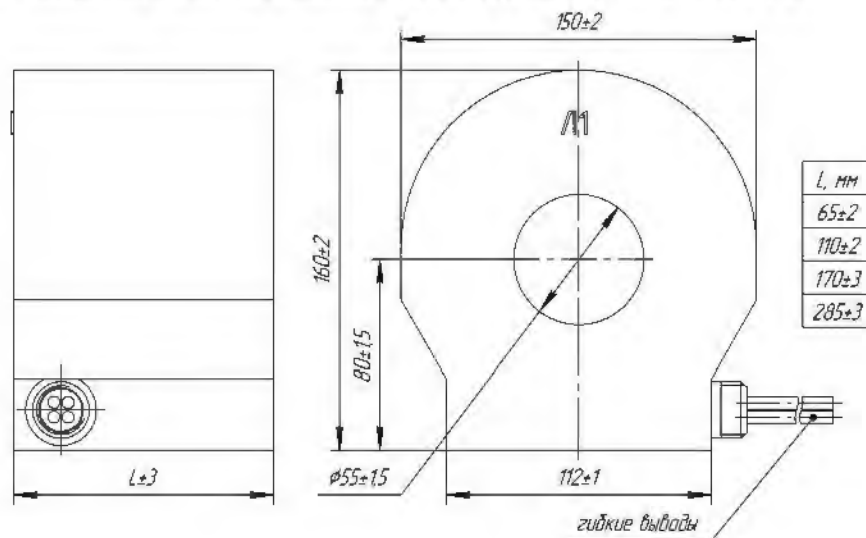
Габаритные и установочные размеры шинного трансформатора ТШ-ЭК-0,66 М4.
